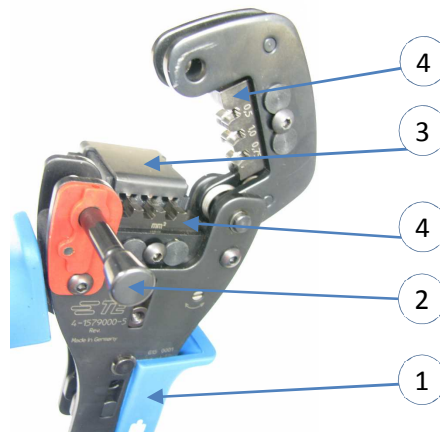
Das Handwerkzeug inkl. Crimpmatrzensatz
